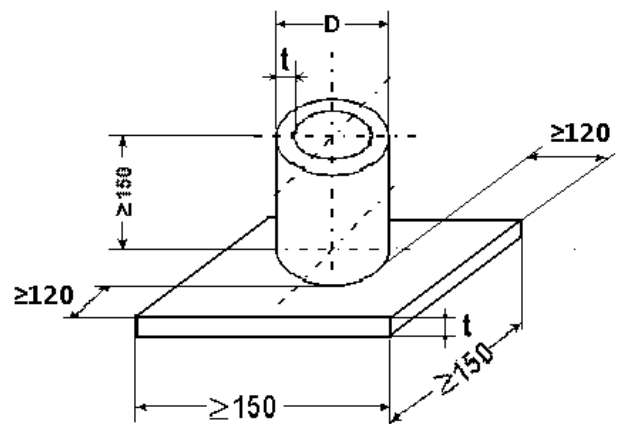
Розміри заготовок для кутових з'єднань з трубою
